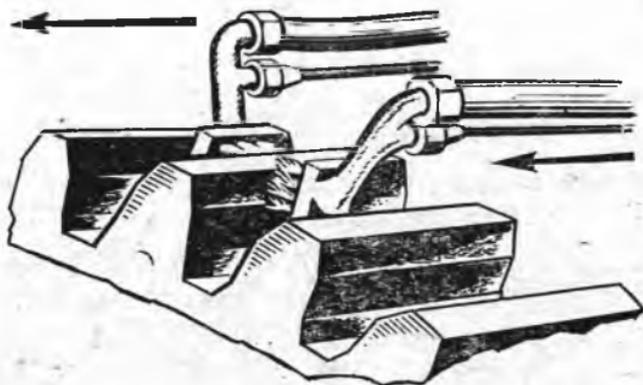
Закалка зубчатого колеса методом «зуб за зубом»
